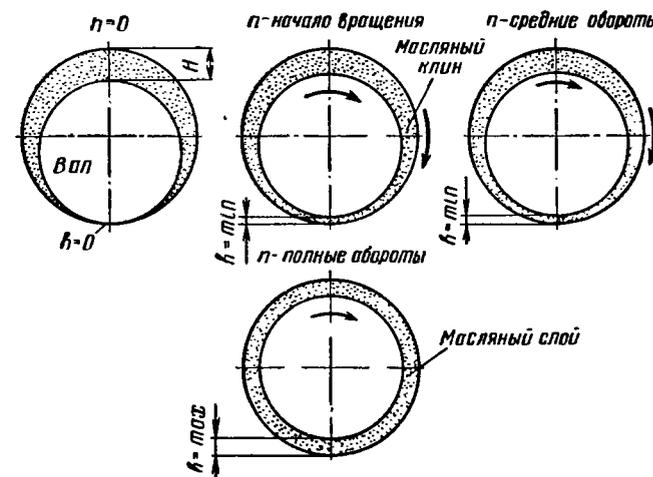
Возникновение несущей способности масляного слоя при вращении вала в подшипнике: h — толщина масляного слоя; n — обороты вала; H — зазор между деталями.
